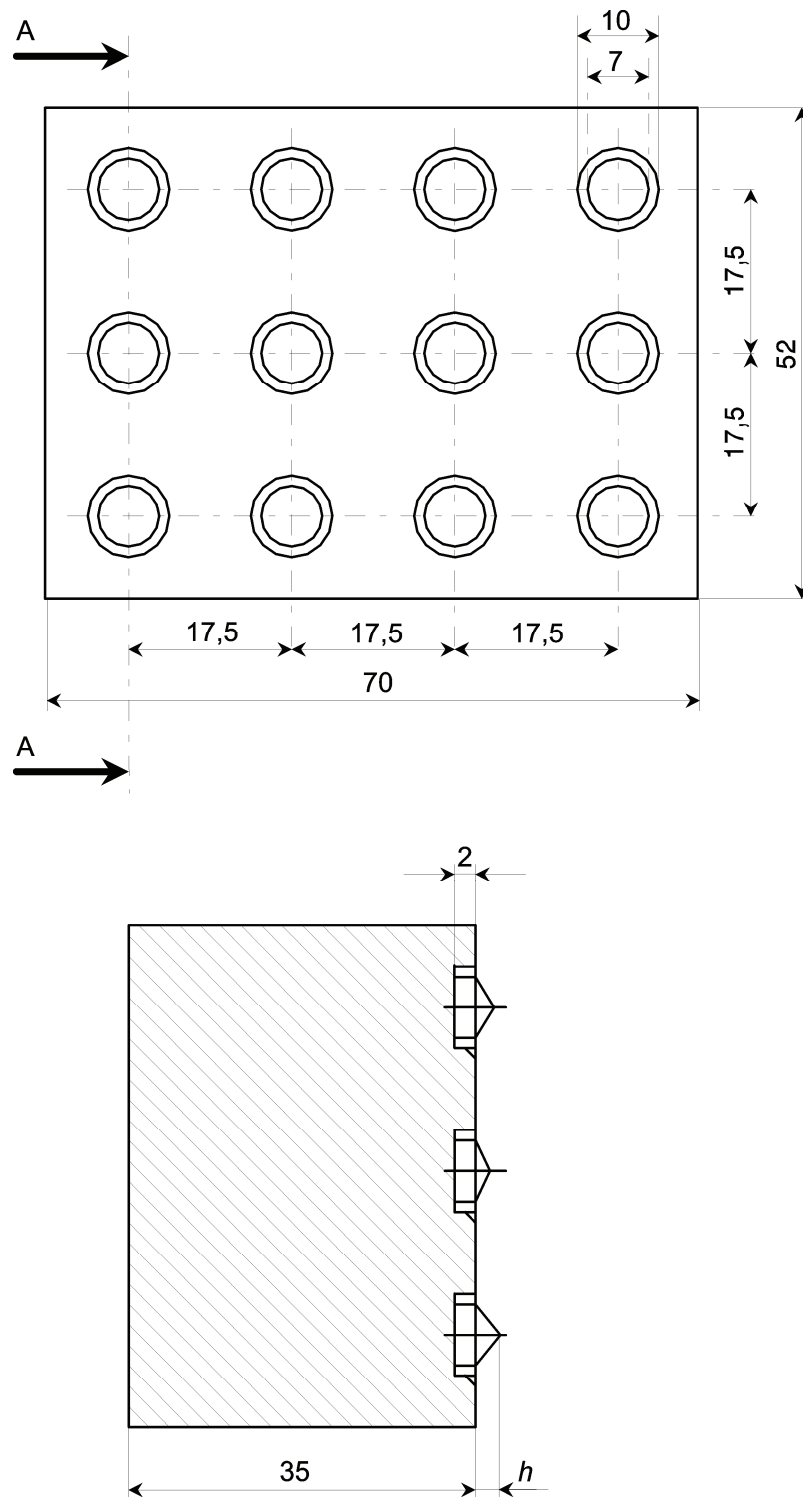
Eindruckplatte für Verformbarkeitsprüfungen
